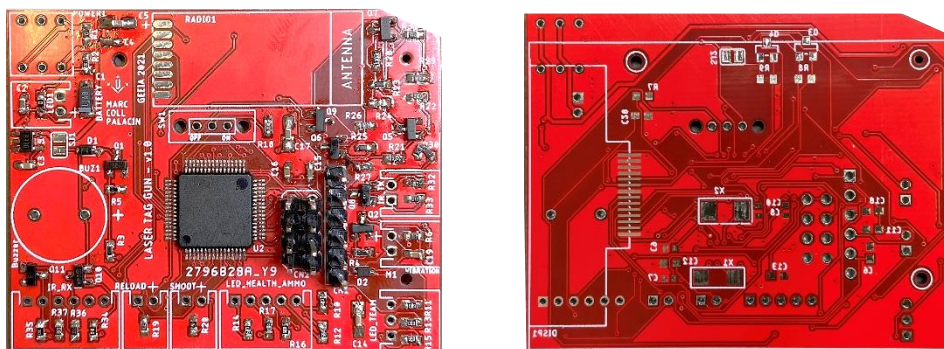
Cara posterior PCB amb components soldats i cara davantera neta
